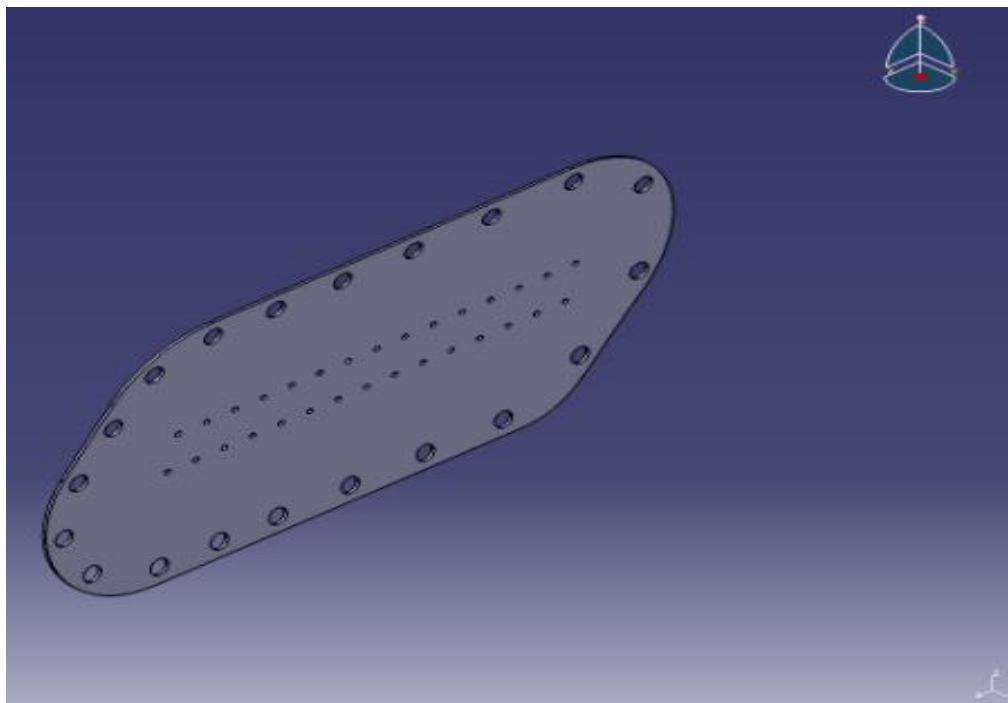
Tapa de inspección original. Fuente: Propia del autor.
